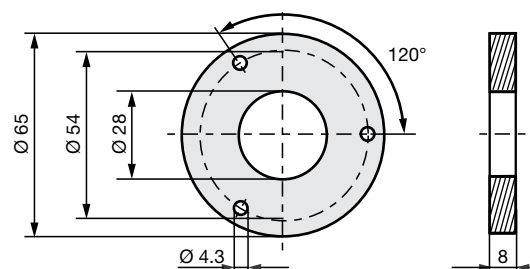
Accessori speciali BTL-P-1028-15R
